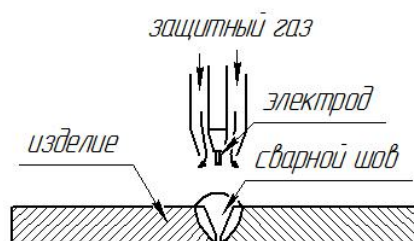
Схема сварки неплавящимся электродом в среде защитного газа
